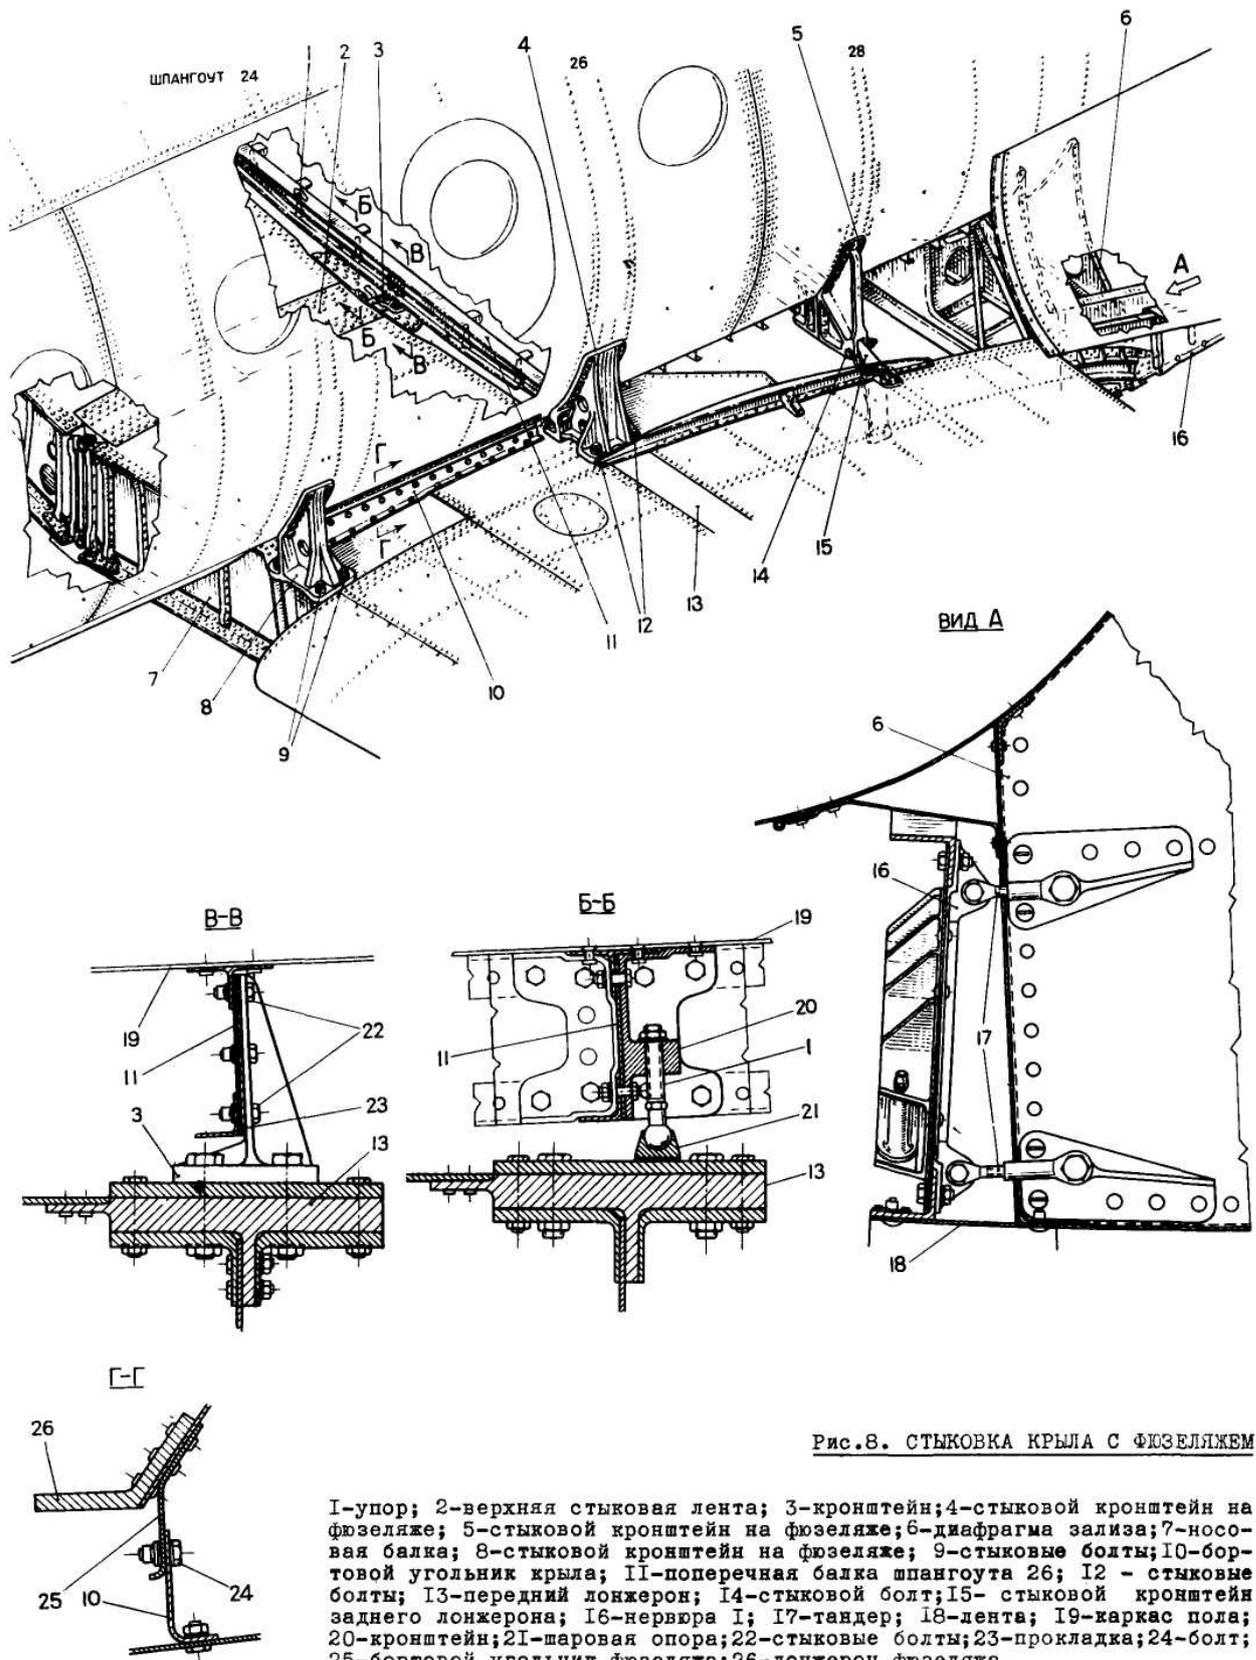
СТЫКОВКА КРЫЛА С ФЮЗЕЛЯЖЕМ
